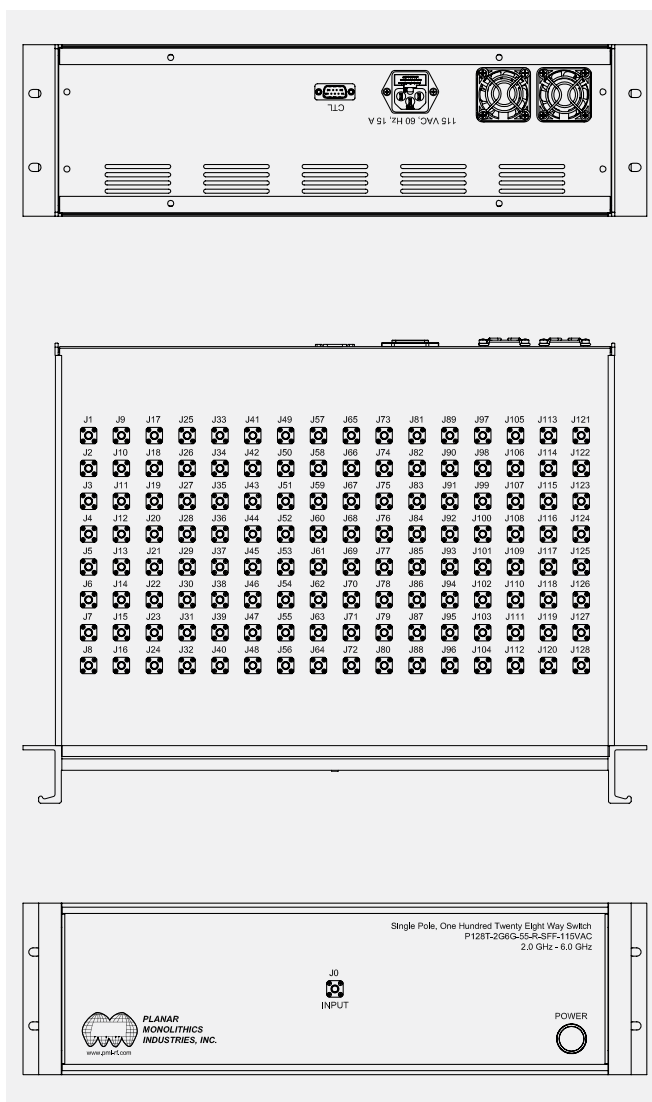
Конструкция 128-позиционного (модель P128T-2G6G-55-R-SFF-115VAC, PMI) переключателя в приборном исполнении с расположением выходных соединителей на верхней крышке прибора
